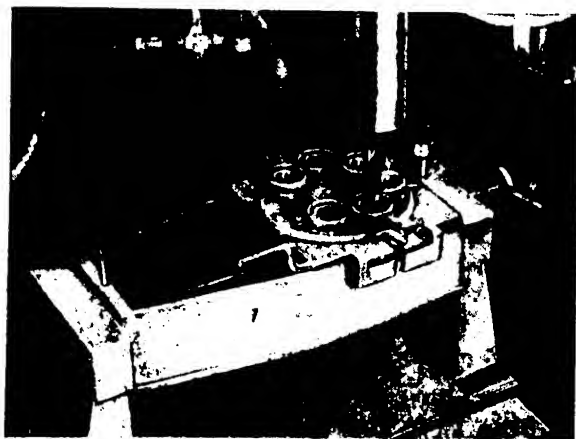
Vorbohren der Bolzenlöcher mittels einer schwenkbaren Kastenbohrlehre
